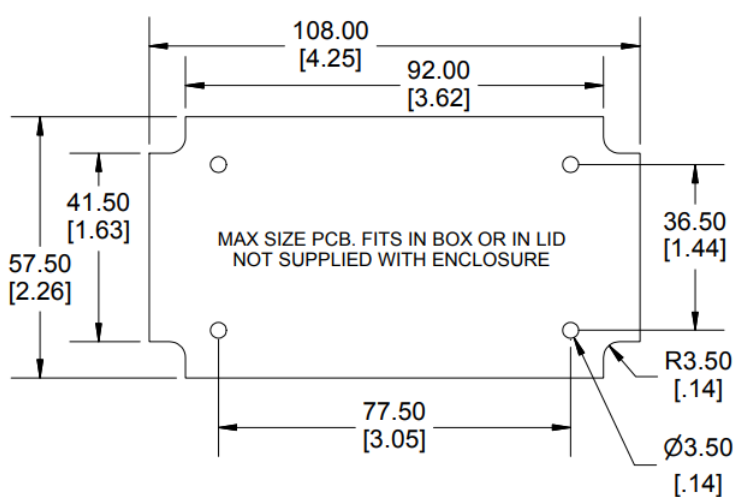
Máximas dimensiones de la PCB dentro de la caja [8]
